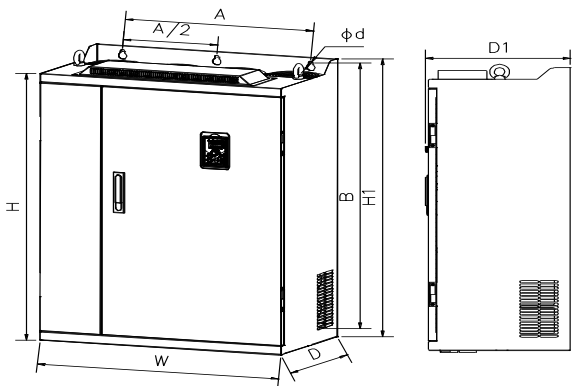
Dimensões 250~400kW G3 (Chassis No.: A12~A13)
